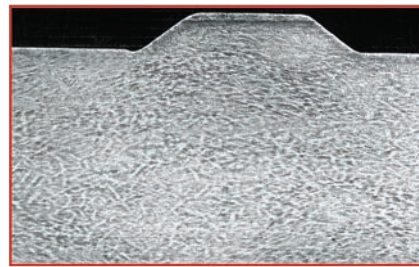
Вид зварного з'єднання сталі з феритною структурою
